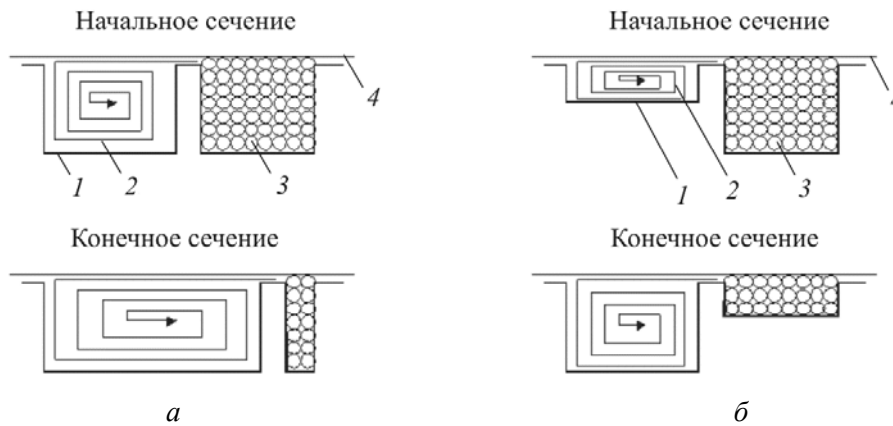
Схема плавления полимера в барьерных шнеках: *а* – Майлифер; *б* – Бар: 1 – шнек; 2 – канал жидкой фазы; 3 – твердая фаза; 4 – корпус
